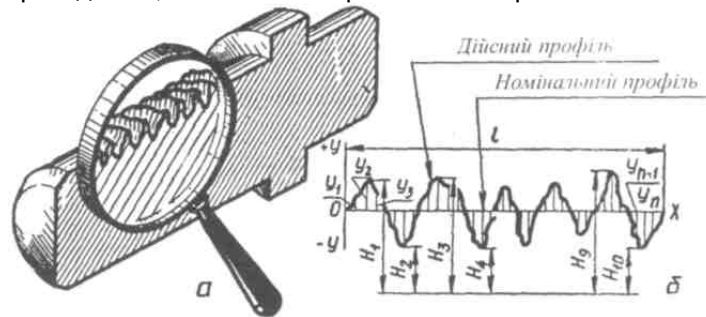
Мікронерівності на поверхні деталі після механічної обробки: а - загальний вигляд; б - схема кількісного оцінювання.
